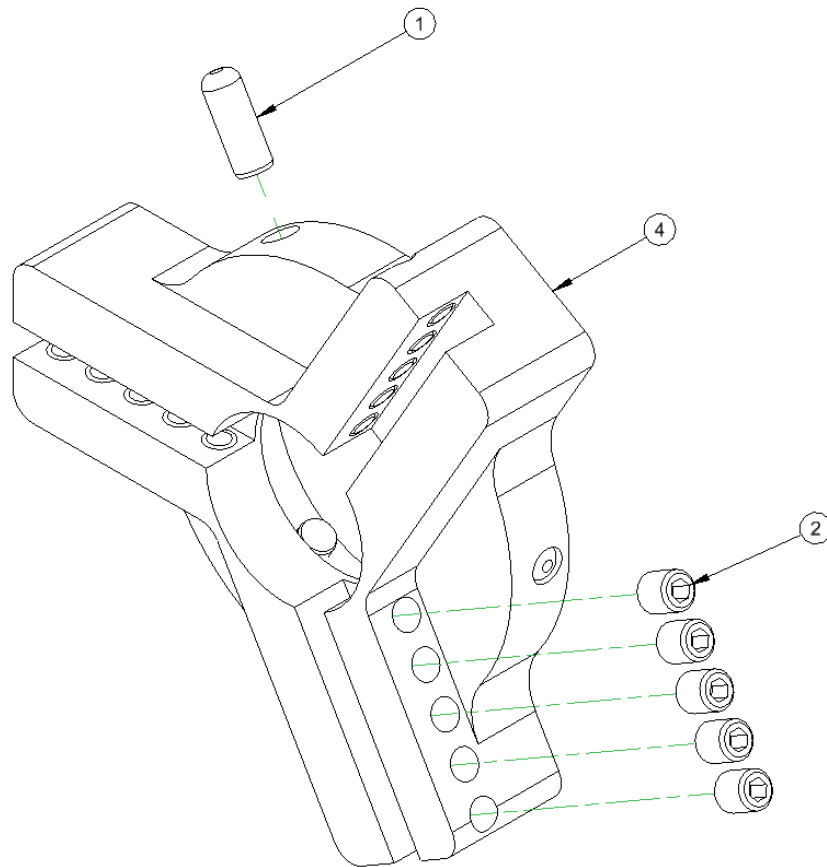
Ensemble de tête du porte-outil (RÉF. 35428)
